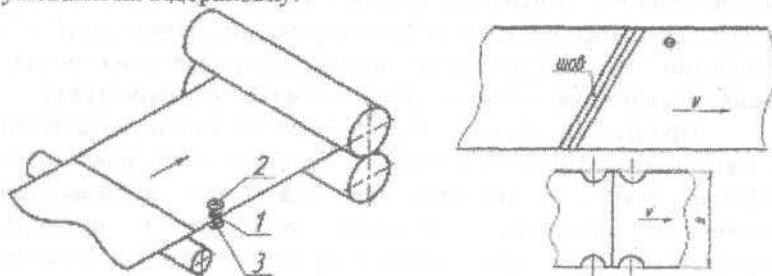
Способи виготовлення отворів для виявлення зварного шва
